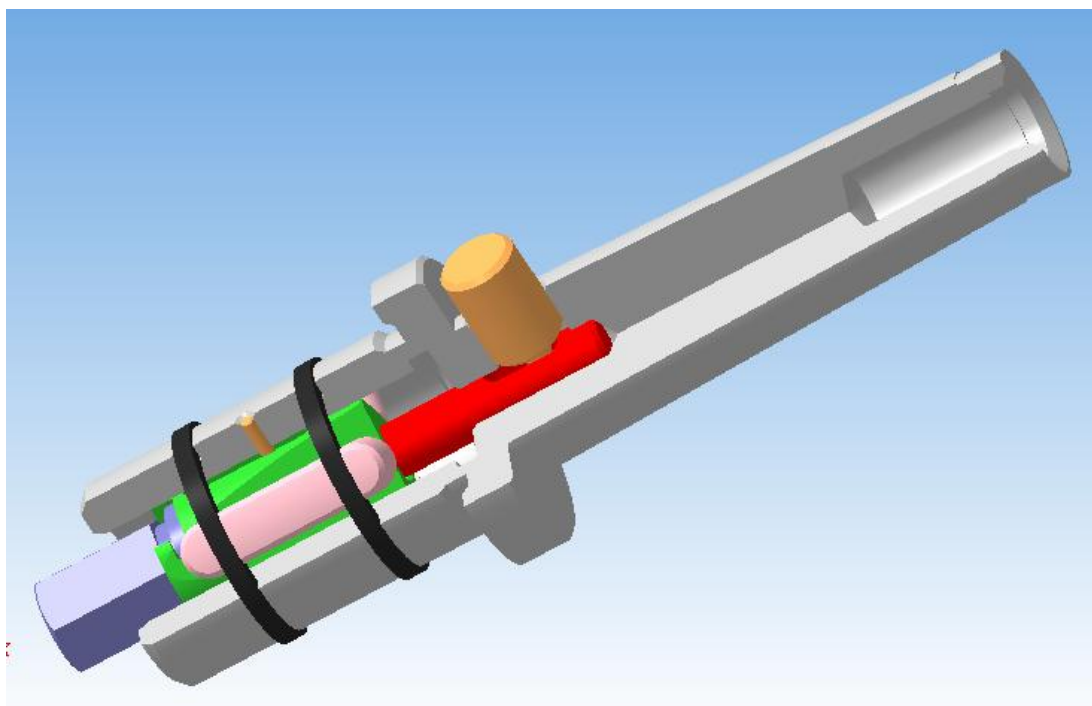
Оправка, 3D сборка с вырезом  $\frac{1}{4}$  части корпуса
